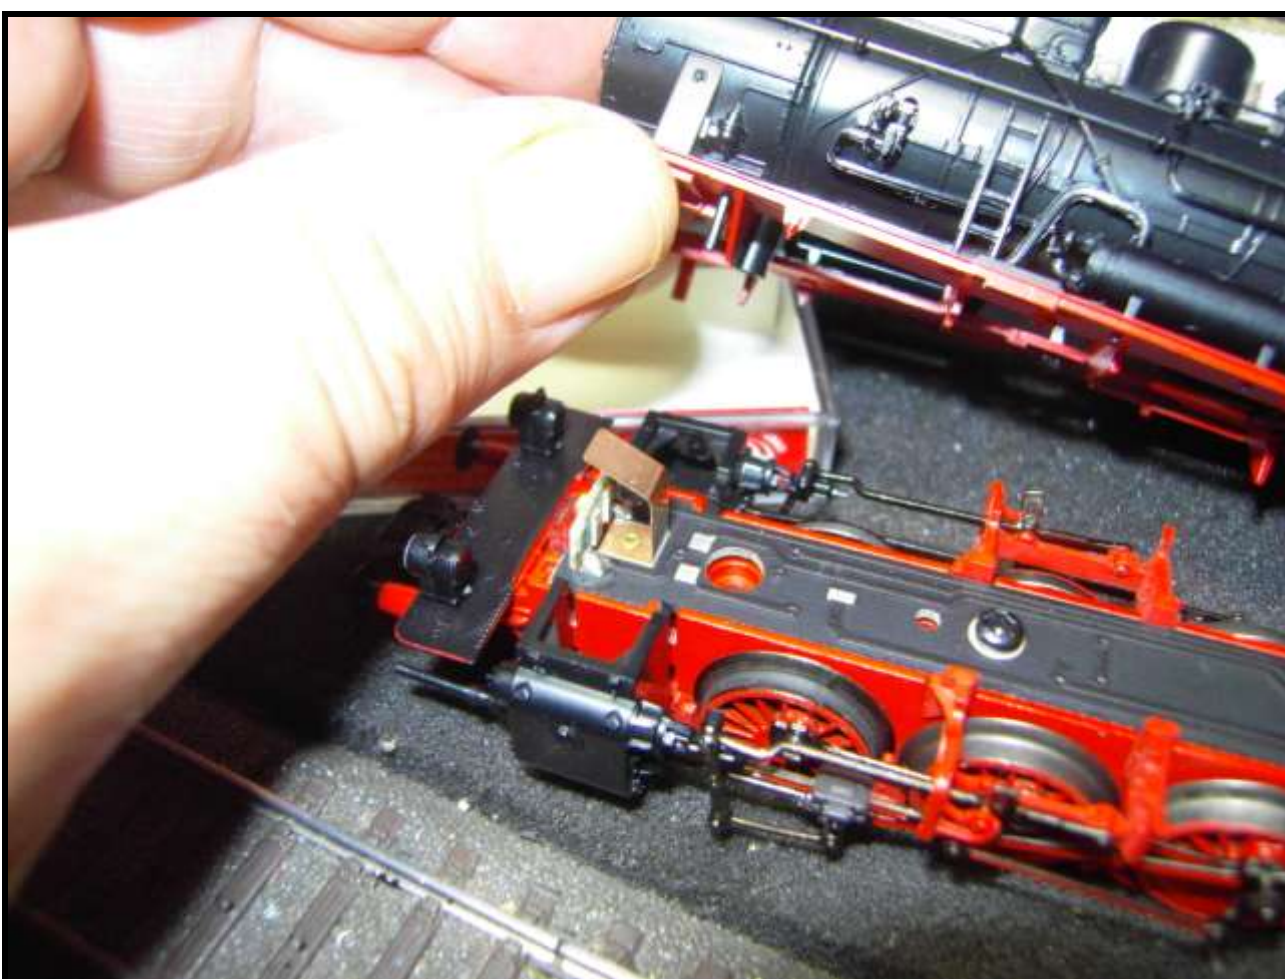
la lamella di contatto fissata nel telaio delle Br 55.
